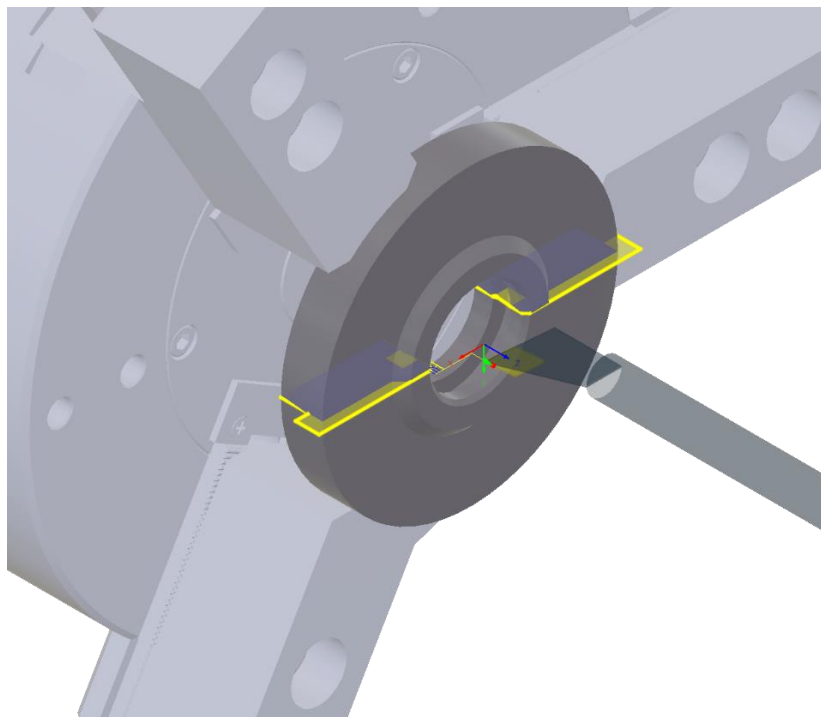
Зображення переходу розточування отвору заготовки
